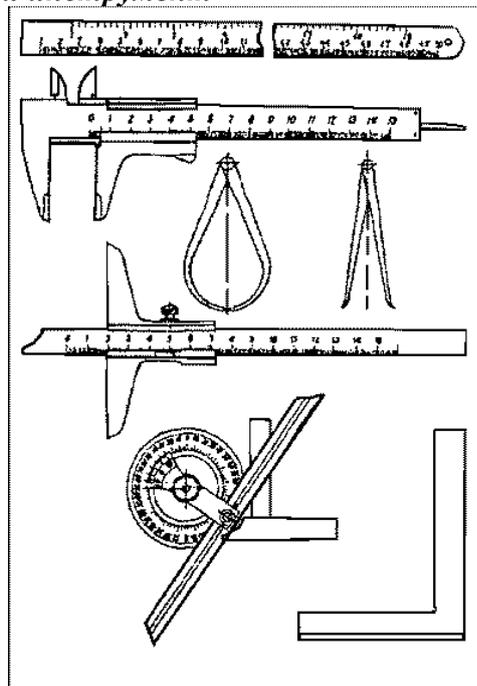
Универсальные измерительные инструменты: а – мерная металлическая линейка; б – штангенциркуль; в – кронциркуль нормальный; г – нутромер нормальный д – штангенглубиномер; е – угломер универсальный; ж – угольник плоский на 90°
